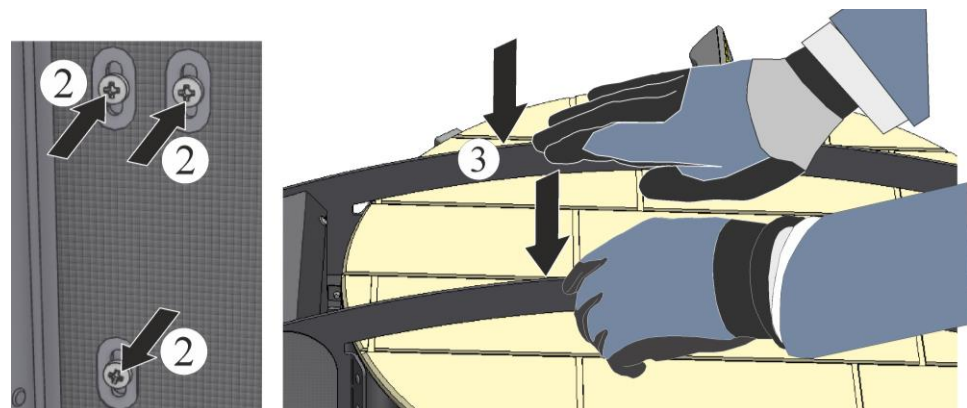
Løsn skruerne/tryk låget imod (eksempelbillede)
